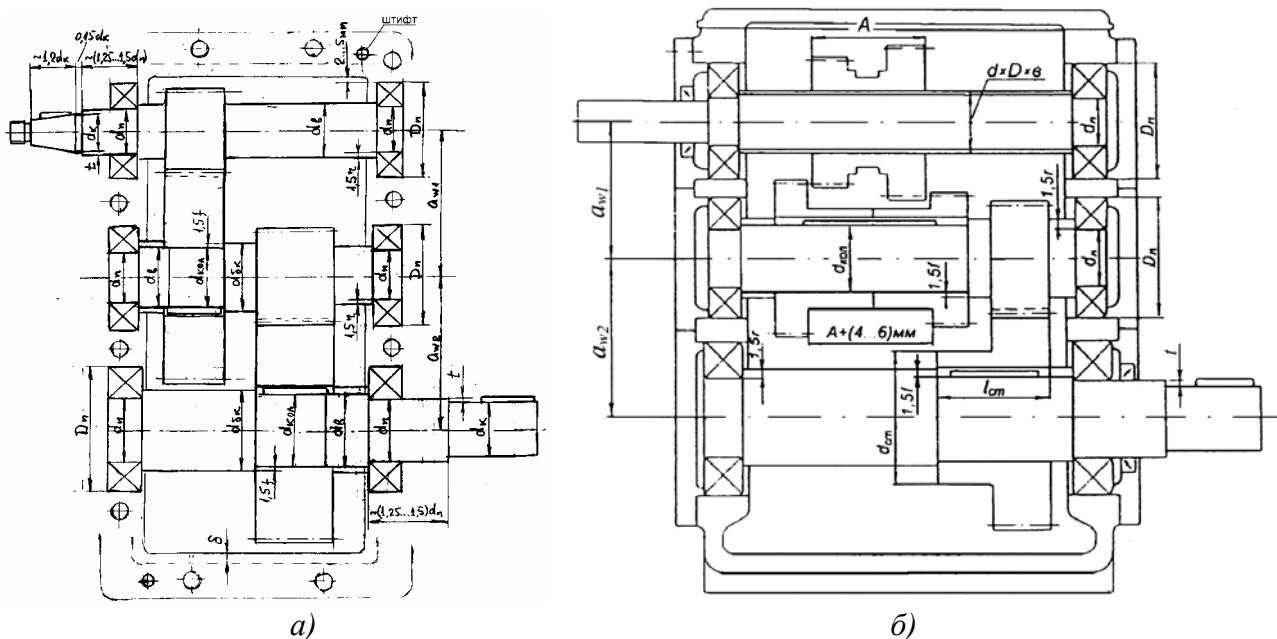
Схемы компоновки редуктора (а) и коробки скоростей (б)
